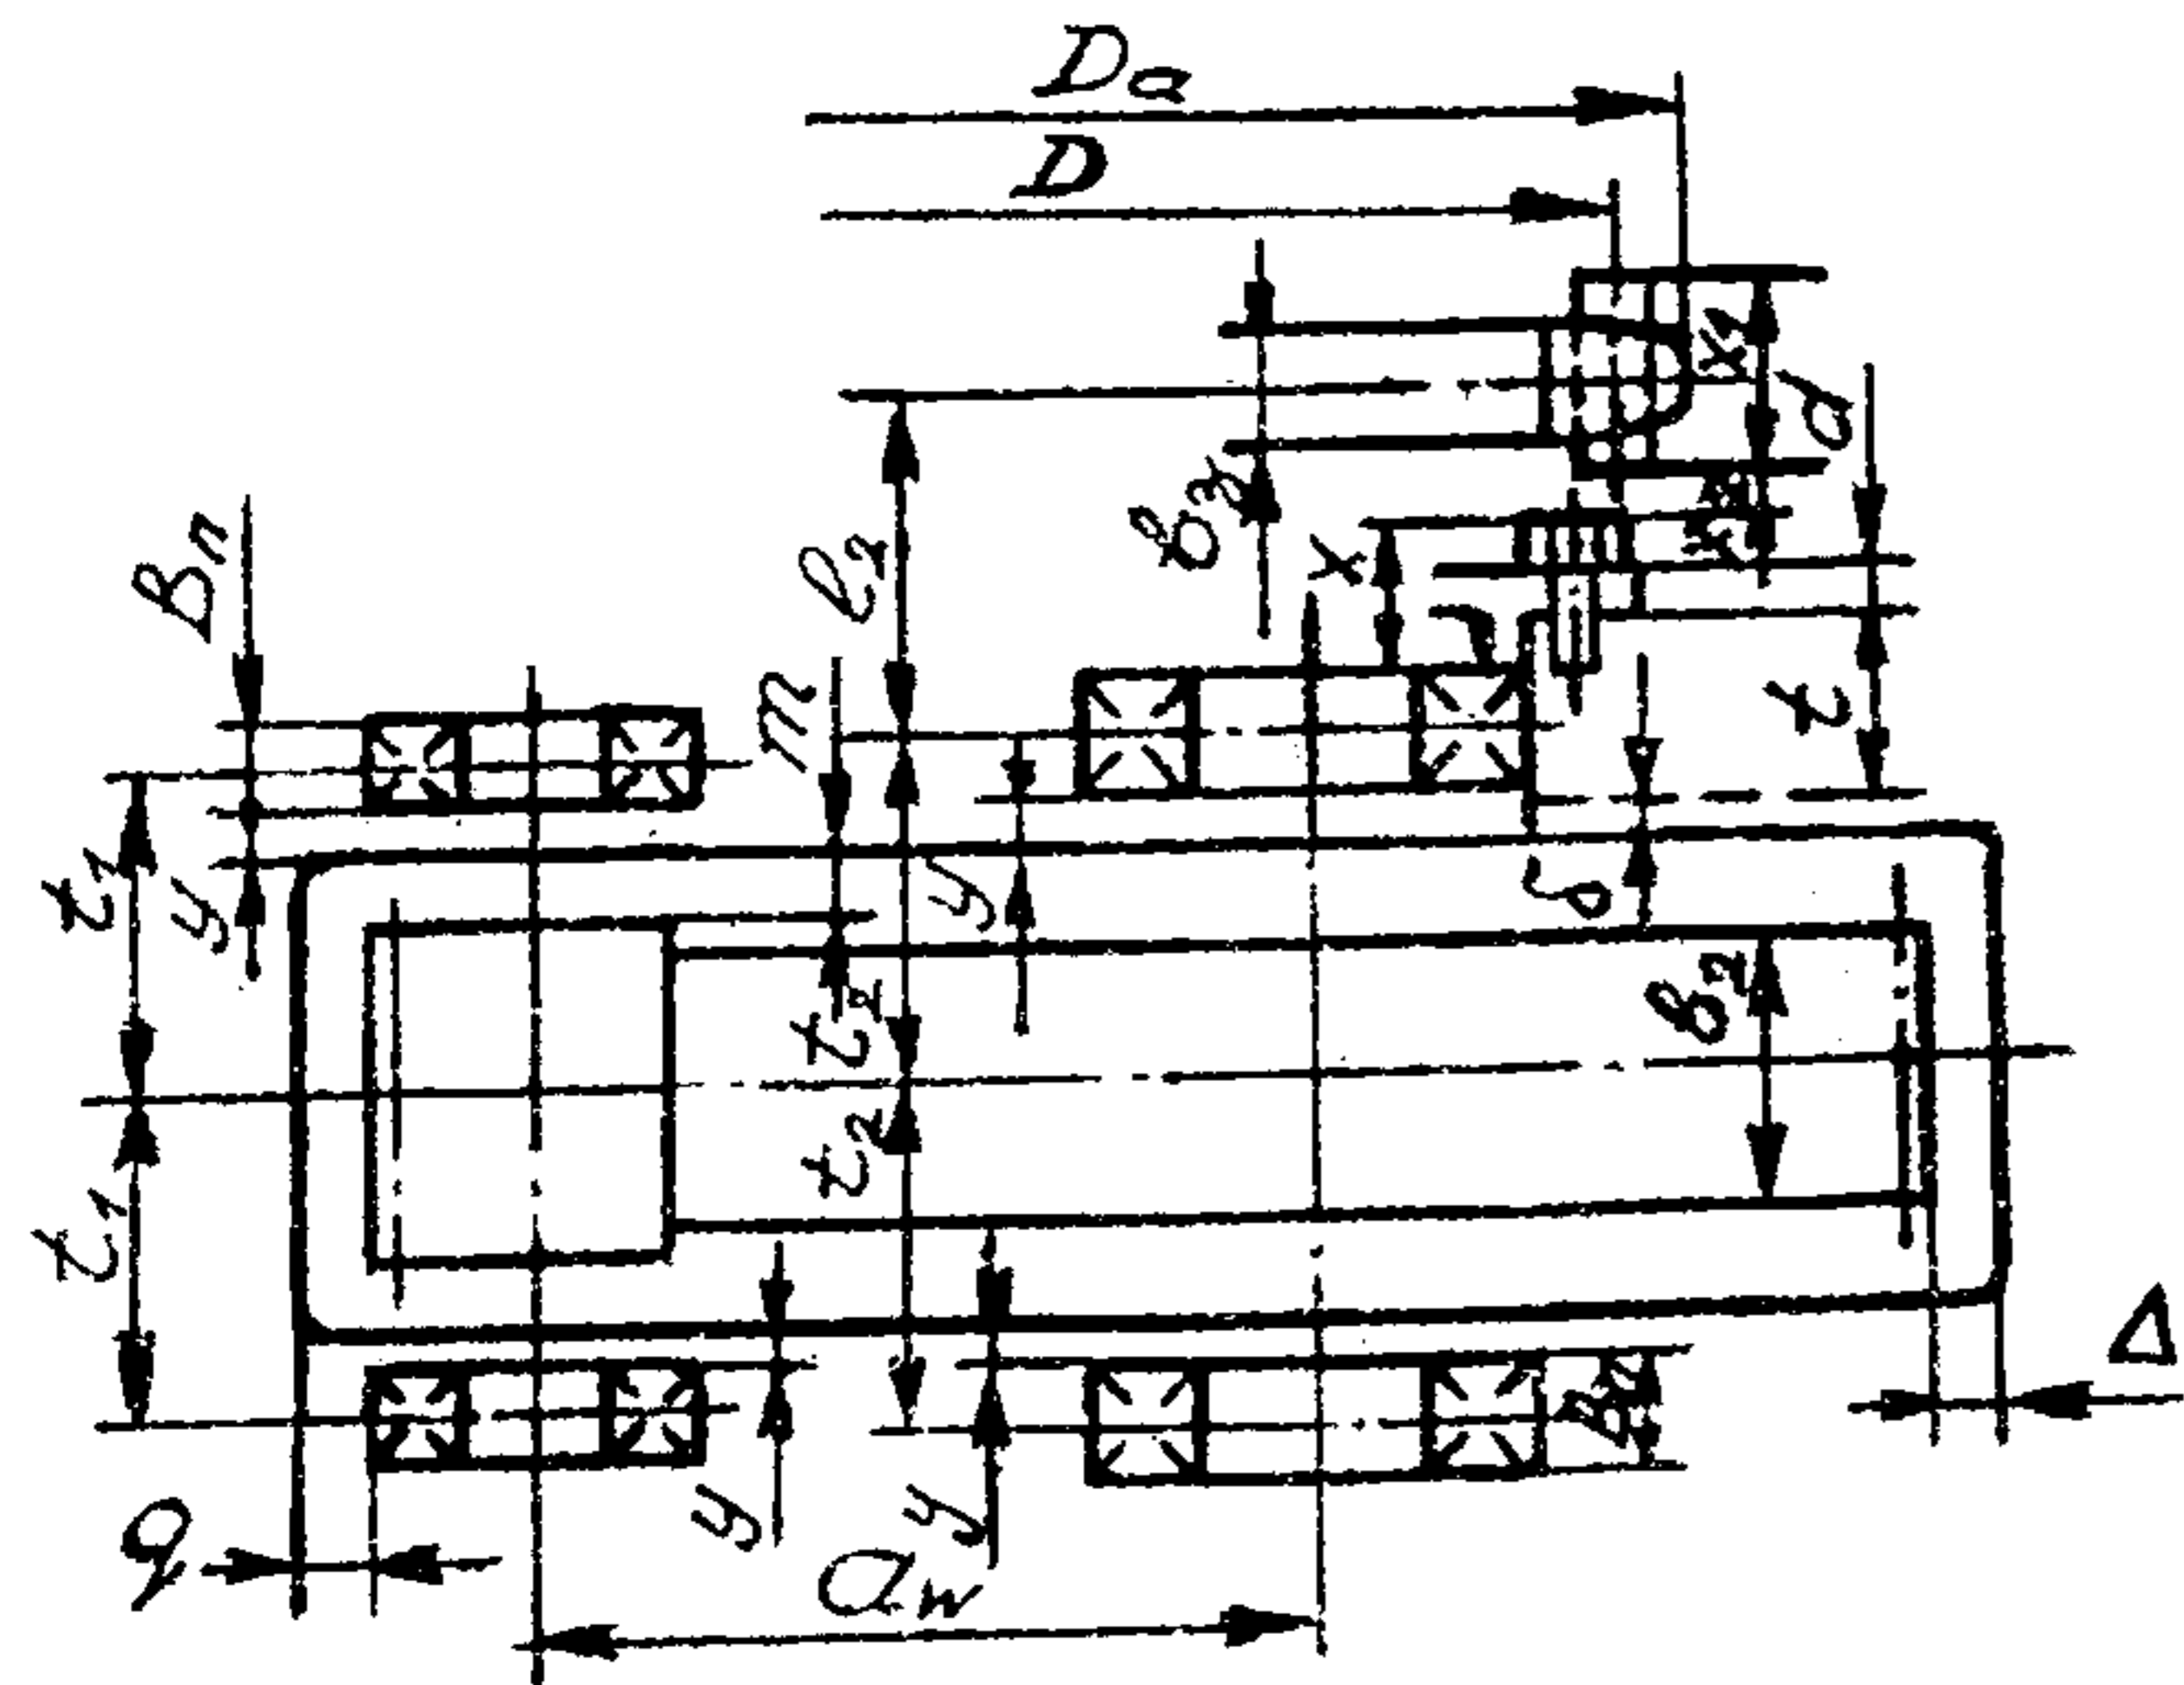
Эскизная компоновка одноступенчатого цилиндрического редуктора
